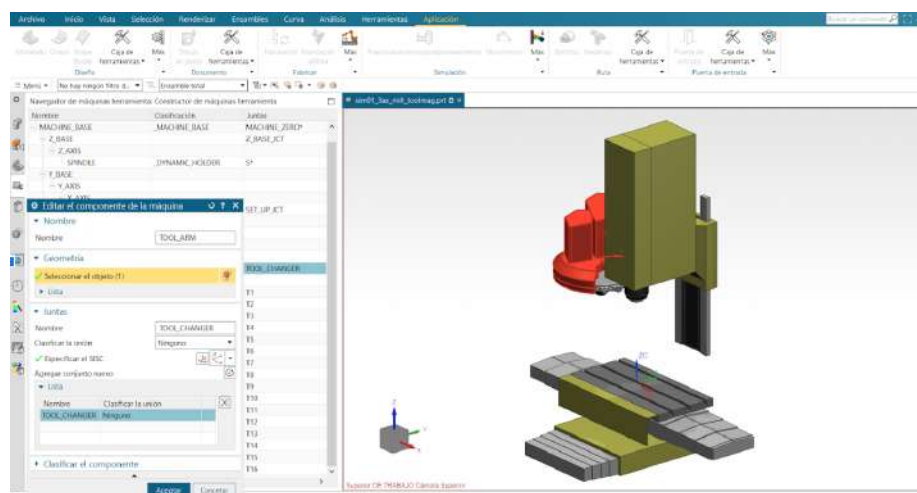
Definición del componente Brazo del Cambiador Automático de Herramientas.
